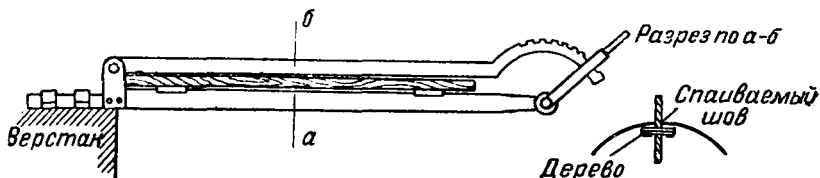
Приспособления для пайки доньшек в цилиндрических изделиях
